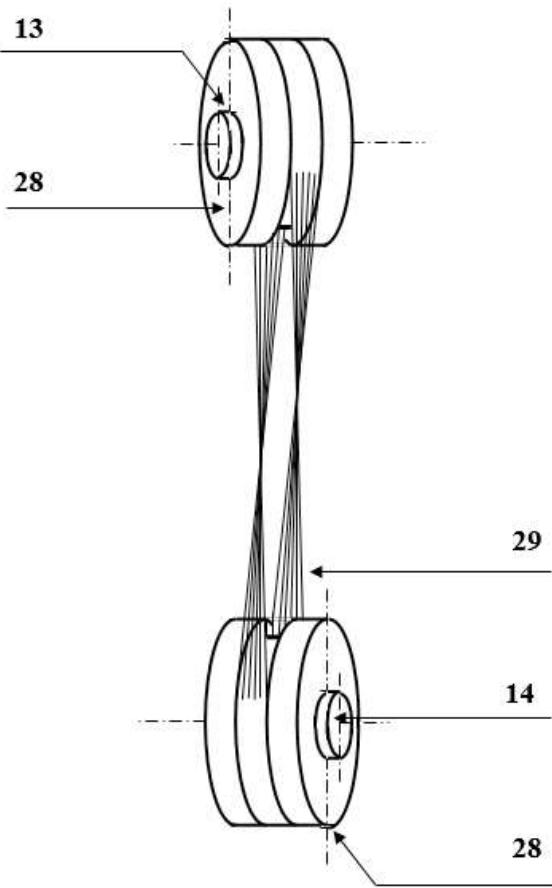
Фрагмент зубчатой клиноременной передачи предложенного распиловочного устройства (вид А):
